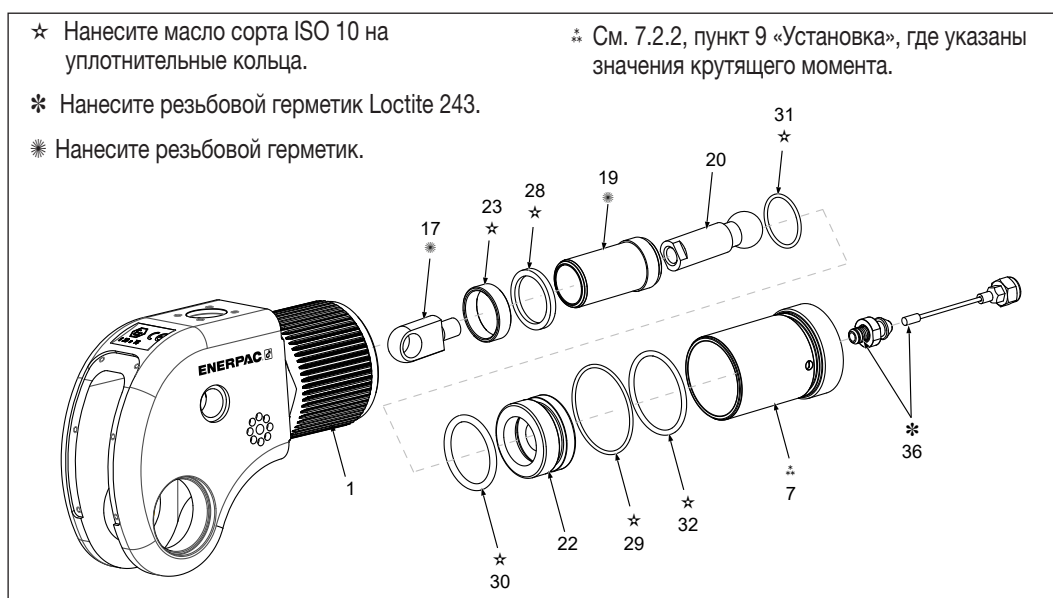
Трехмерное представление цилиндров DSX1500, DSX3000, DSX5000
